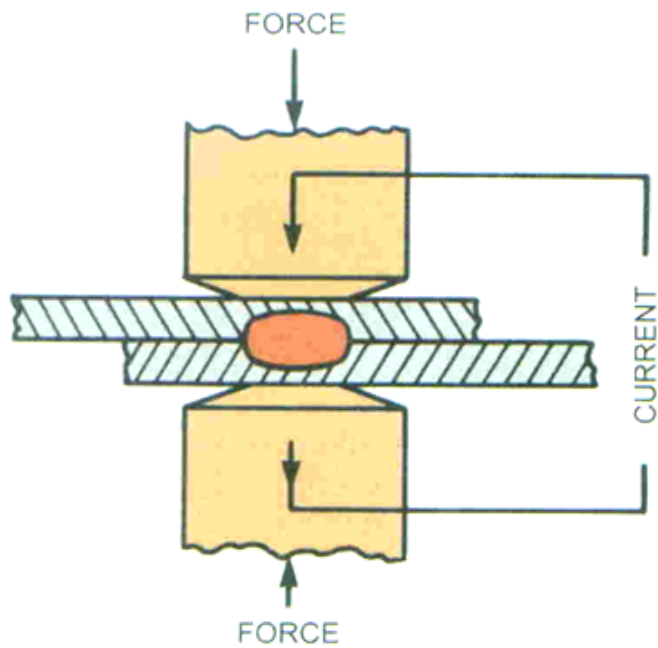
Esquema de soldadura de punto (researchgate.net).
